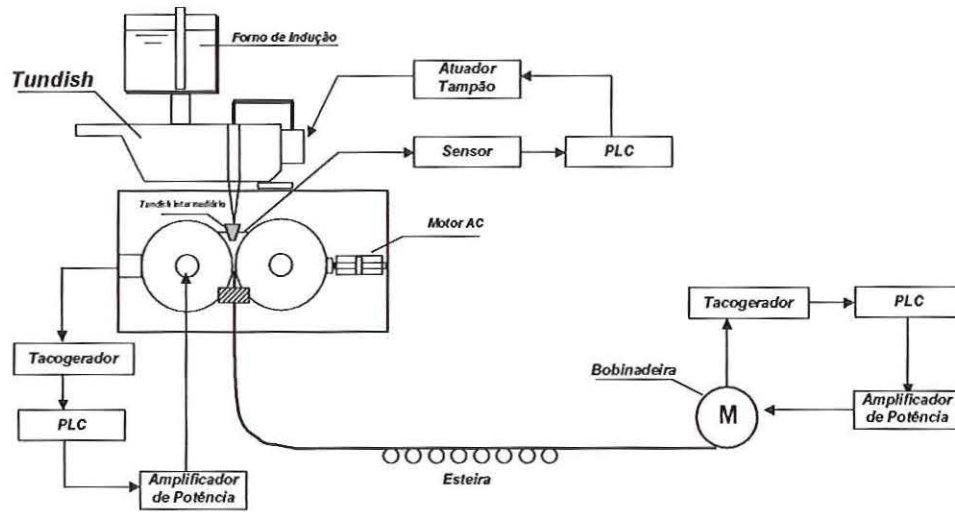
Esquema da planta piloto de LCT-RD instalada no IPT-SP.
